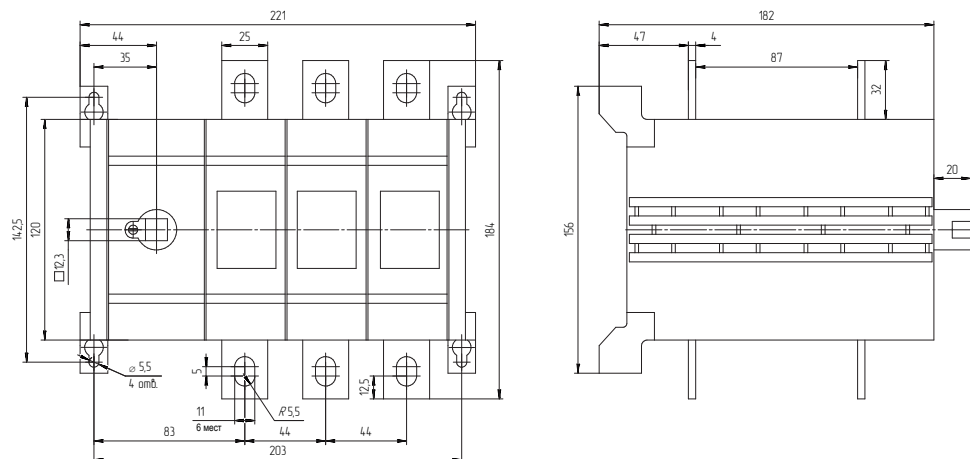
Выключатель-разъединитель 315 – 400 А реверсивного исполнения
